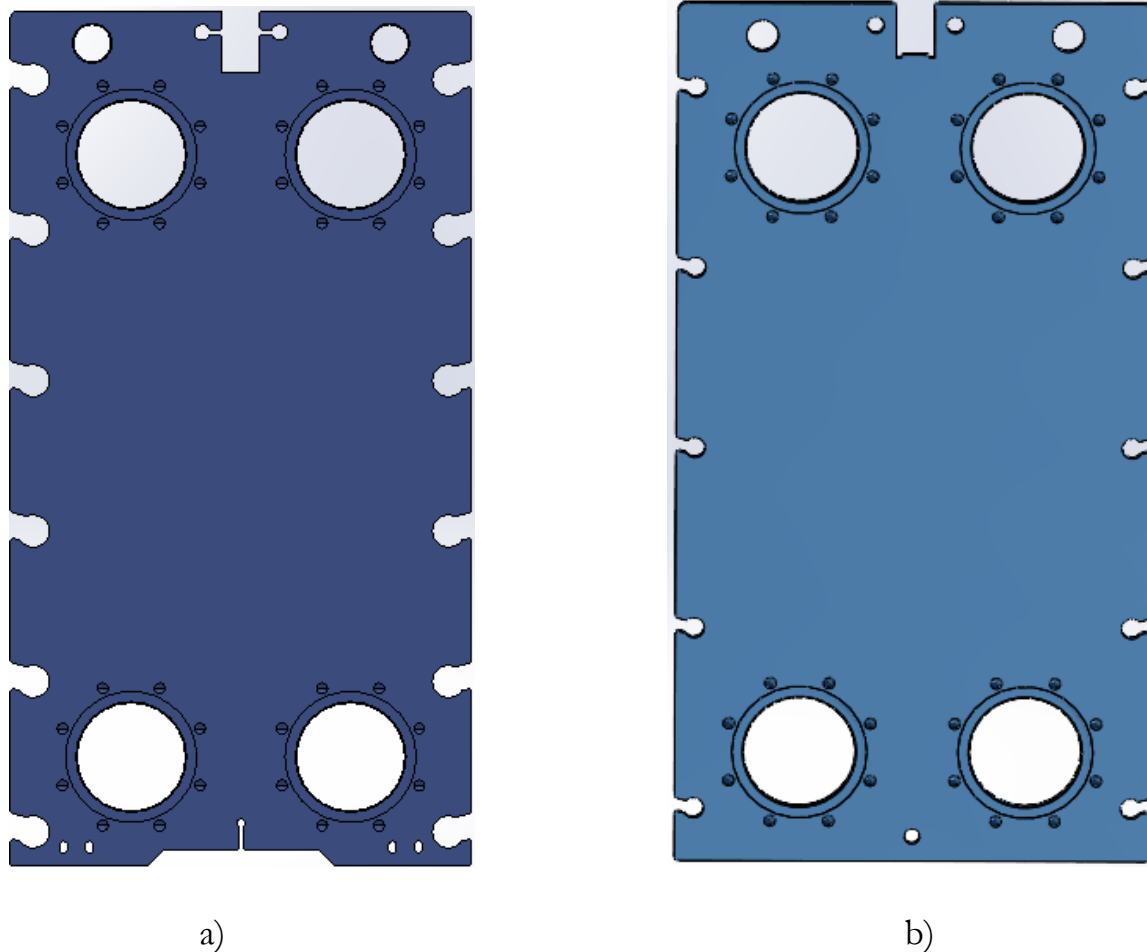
Placa fixa: a) WH30; b) desenhada.
